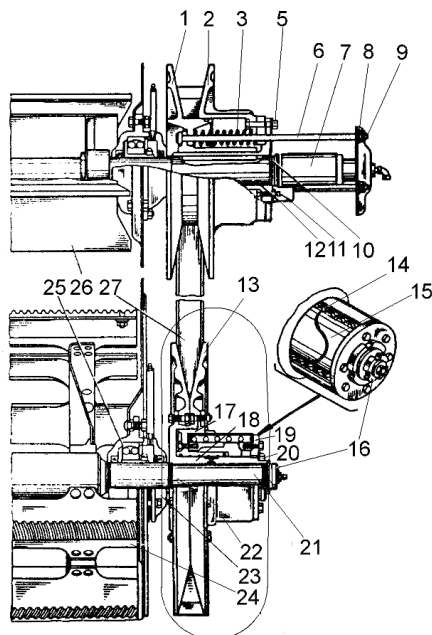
Вариатор молотильного барабана: 1 – подвижный диск ведущего шкива; 2 – неподвижный диск; 3 – пружина; 5, 6 – специальные болты; 7 – гидроцилиндр; 8 – фланец; 9, 20 – гайки; 10 – стопорная шайба; 11 – болт; 12 – вал битера; 13 – диск ведомого шкива; 14 – пружина; 15 – муфта; 16 – гайка; 17 – неподвижная ступица; 18 – подвижная ступица; 19 – крышка; 21 – вал барабана; 22 – кожух; 23 – опора вала; 24 – молотильный барабан; 25 – опорный подшипник; 26 – отбойный битер; 27 – ремень
